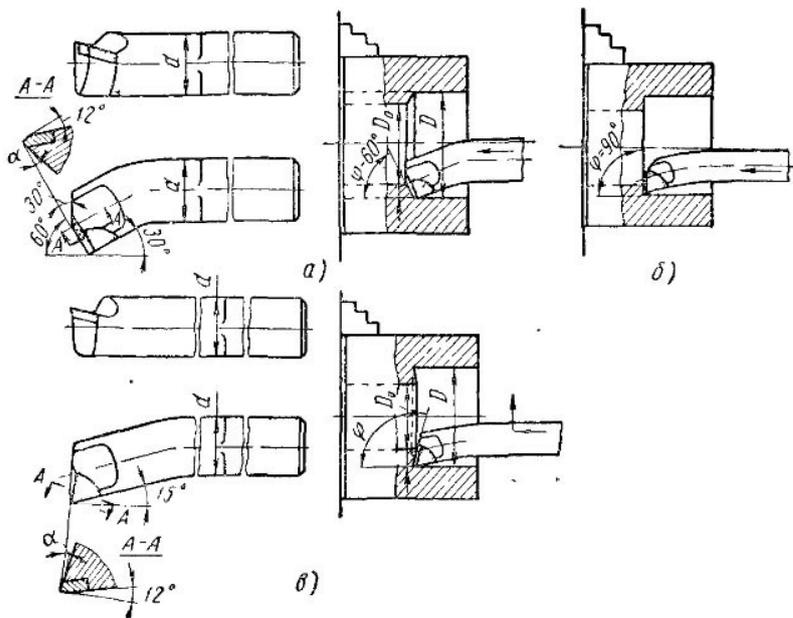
Расточные резцы, оснащенные пластинами твердого сплава: а - проходной для обработки сквозных отверстий, б и в - упорно-проходной для обработки глухих отверстий
